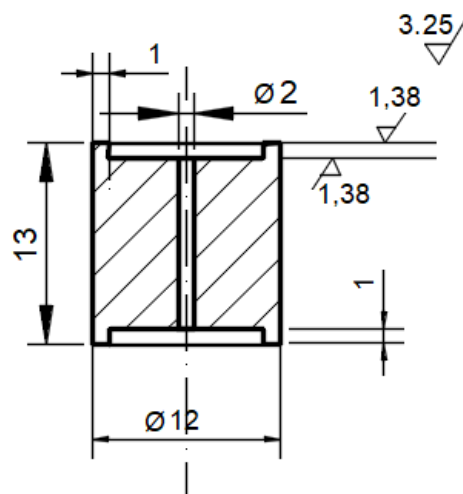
Цилиндрический образец для испытания на сжатие [2].
